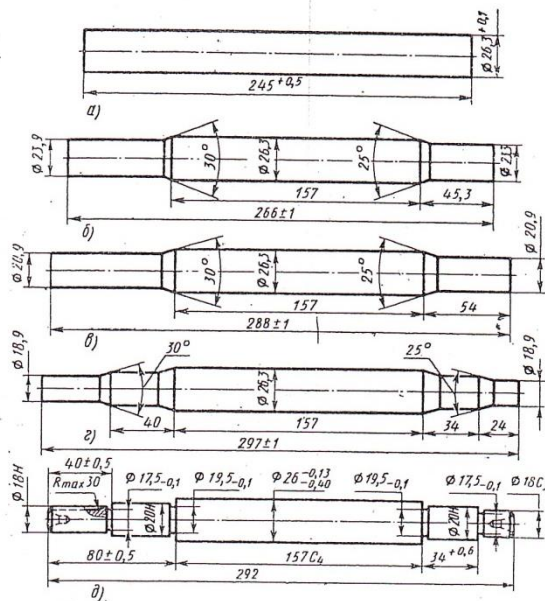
Технологические переходы: а-исходная заготовка; б,в,г – переходы редуцирования; д-готовый вал, полученный после обработки заготовки на металлорежущих станках.
